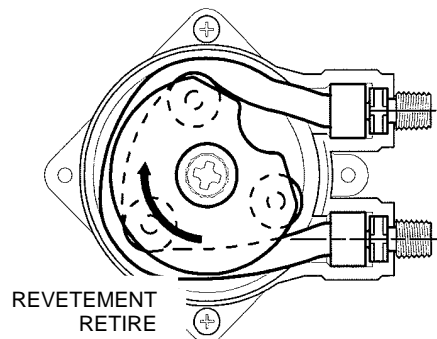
Assemblage de tête de pompe dont le revêtement sur l'avant de l'assemblage a été retiré
